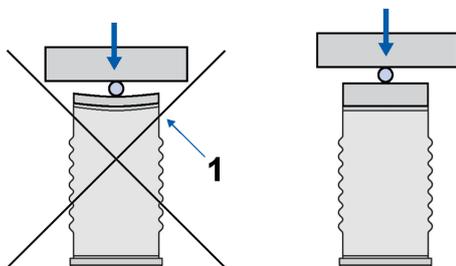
Richtiges Dimensionieren der Endstücke bei punktförmigem Kontakt (1: Zugspannungen)
